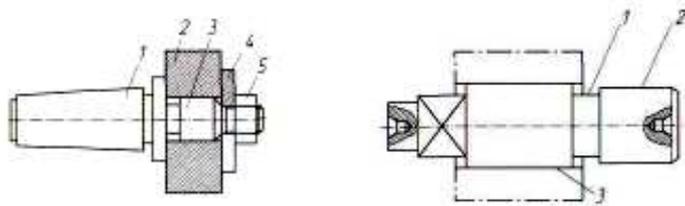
Схемы оправок для установки заготовок: *а* – консольная оправка с зазором: 1 – хвостовик; 2 – заготовка; 3 – рабочая шейка; 4 – быстросъемная шайба; 5 – гайка; *б* – схема цилиндрической прессовой оправки: 1 – кольцевая выточка; 2 – шейка направляющая; 3 – рабочая поверхность
